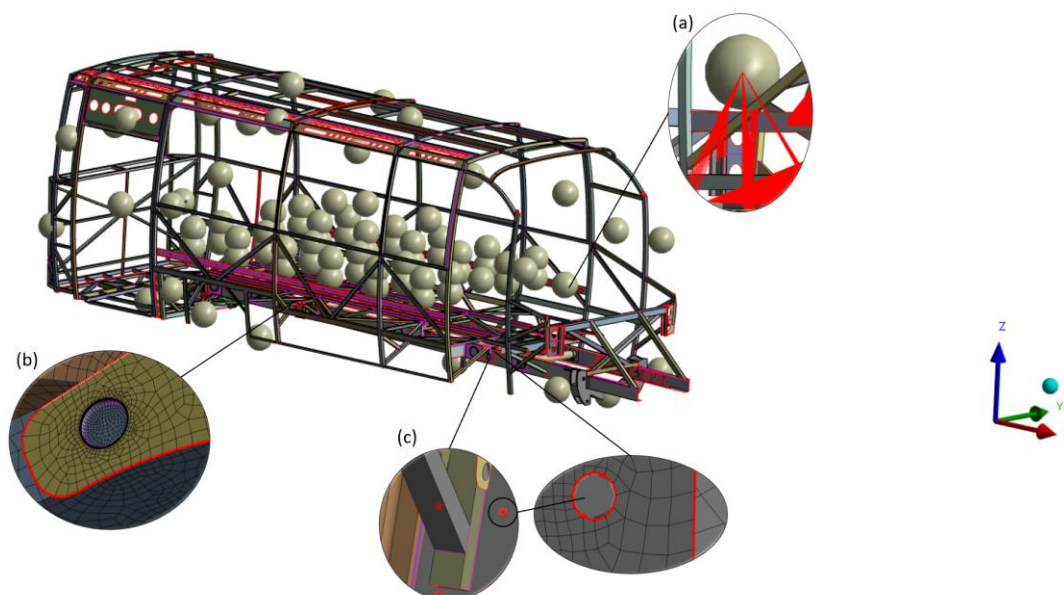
Modelo de elementos finitos da superestrutura mais carroçaria com: (a) pormenor de uma massa remota; (b) pormenor da ligação soldada e (c) de uma ligação aparafusada
